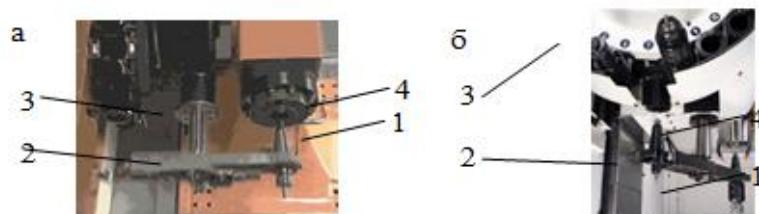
Конструктивная схема смены инструмента манипулятором: 1 – инструмент; 2 – манипулятор; 3 – магазин; 4 – шпиндель
